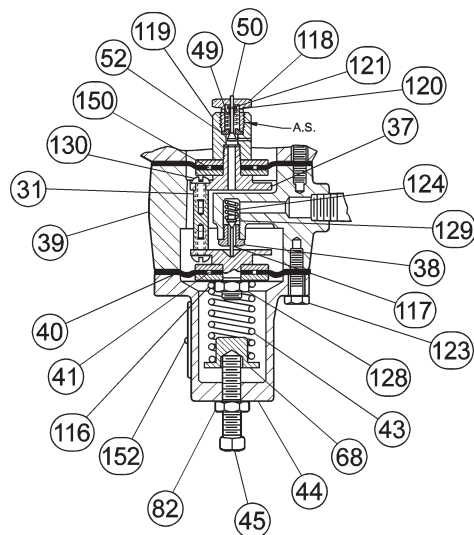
Pilote type 61HP (pilote pour très haute pression)
